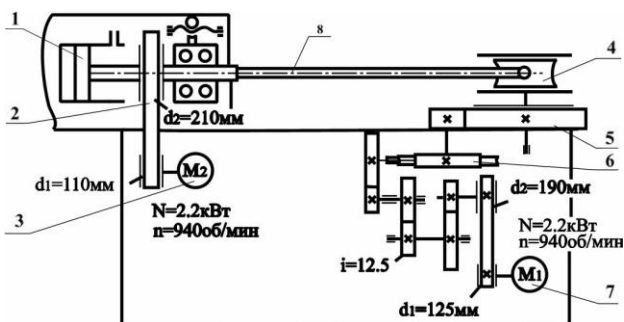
Кинематическая схема модернизированного станка ИВ-3428:
